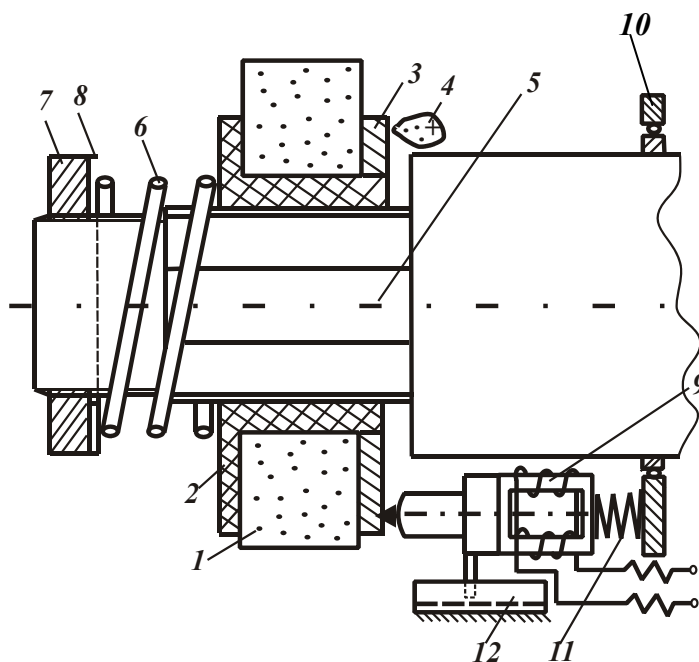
Устройство с осевым перемещением шлифовального круга: 1 – круг; 2 – шлифовальная втулка; 3 – прижимная шайба; 4 – эксцентрик (показан повернутым на 90°); 5 – шлицевый вал с резьбой; 6 – пружина; 7 – гайка; 8 – шайба; 9 – магнестрикционная колебательная система; 10 – подшипник; 11 – пружина; 12 – направляющие.
